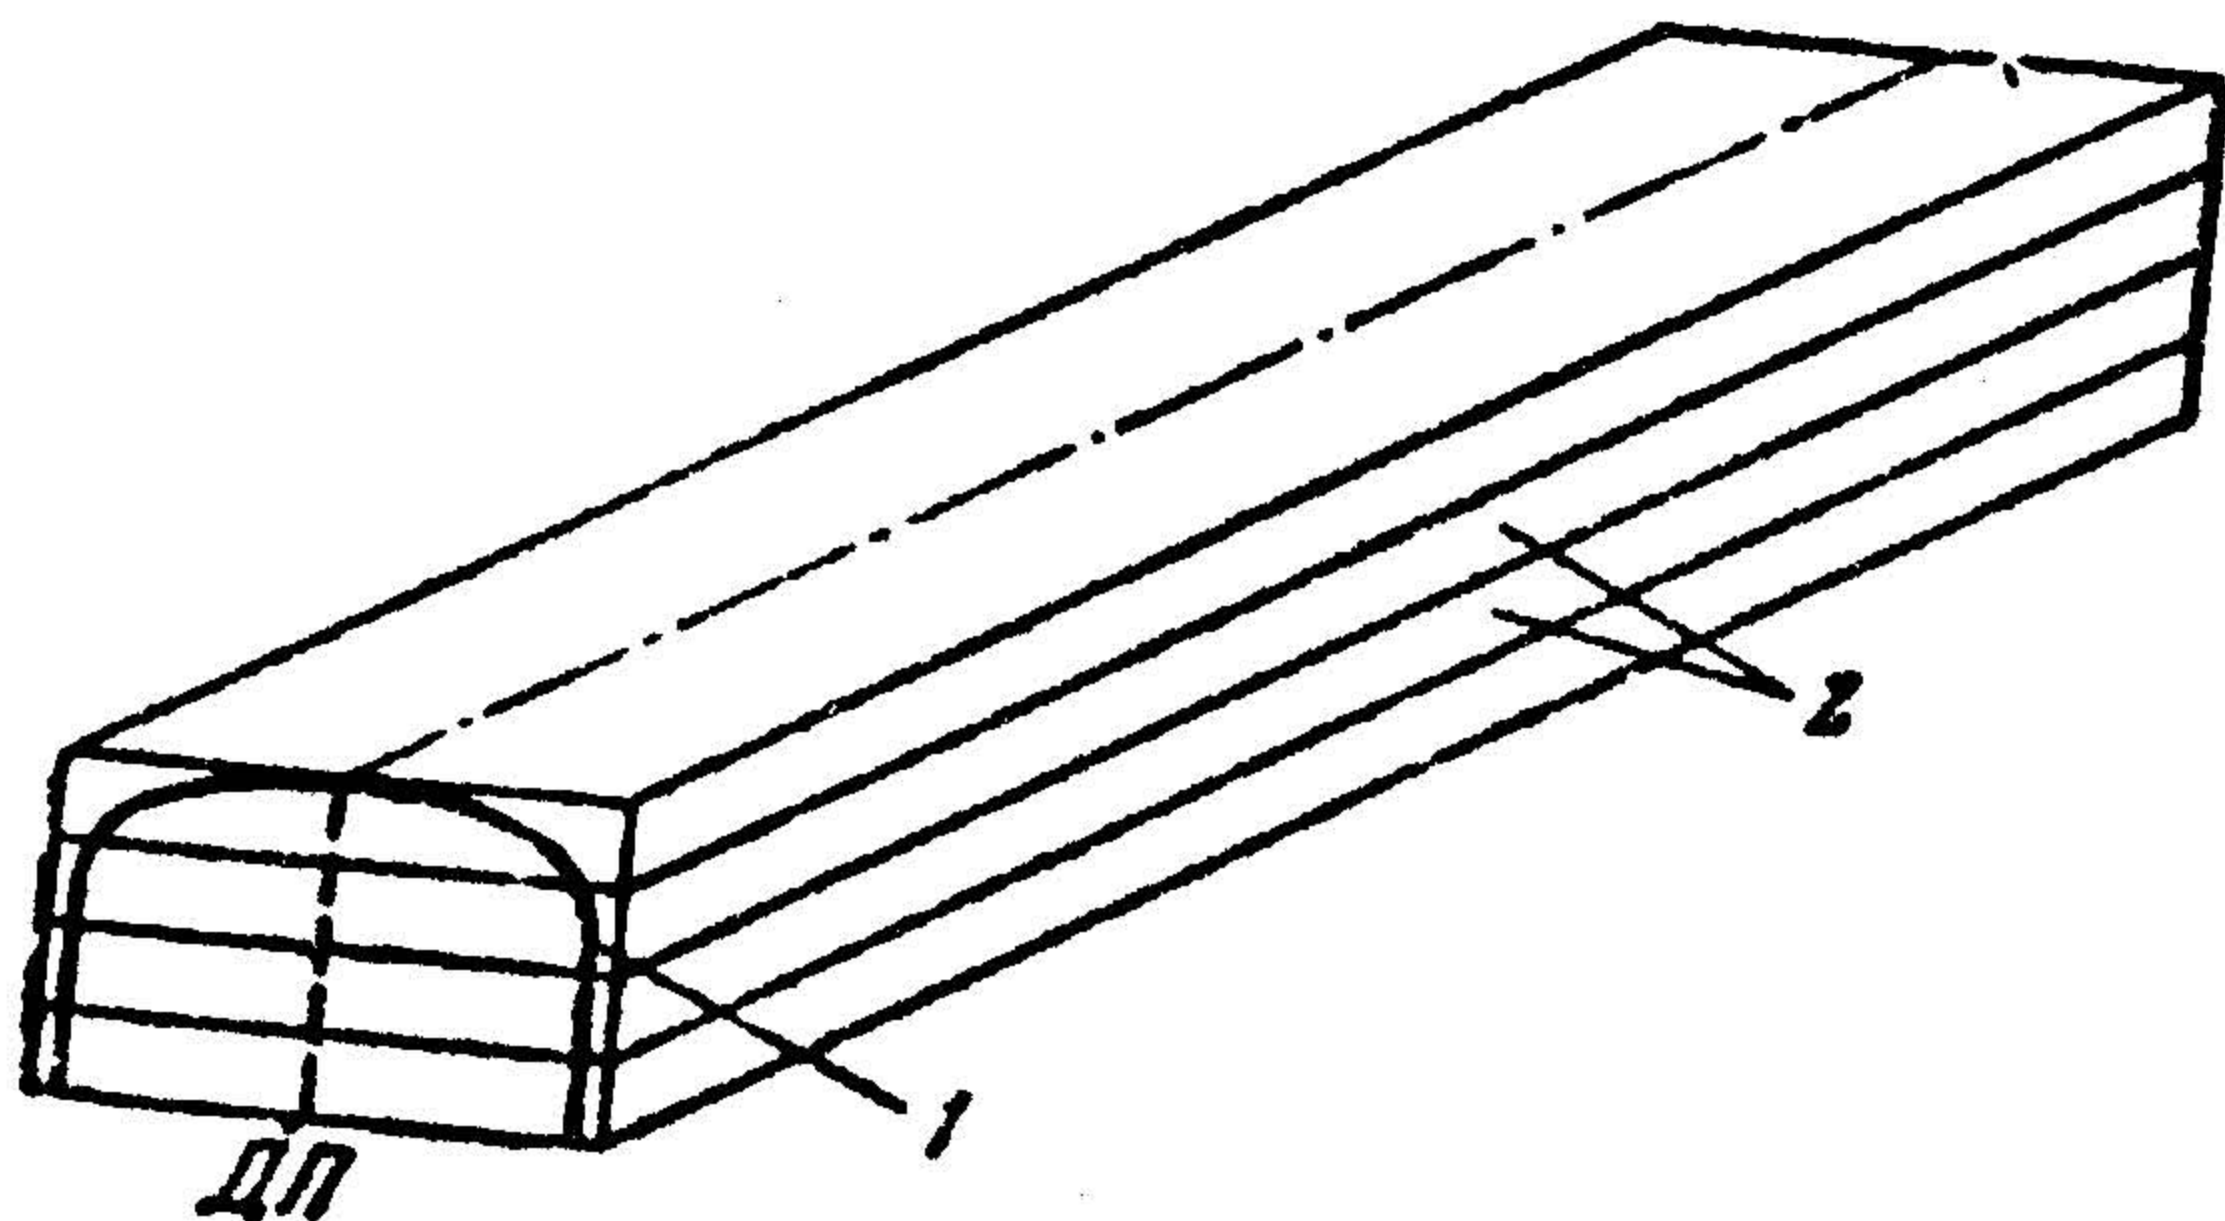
Пакет досок ватерлиний; 1 — контур модель-шпангоута; 2 — доски-ватерлинии
